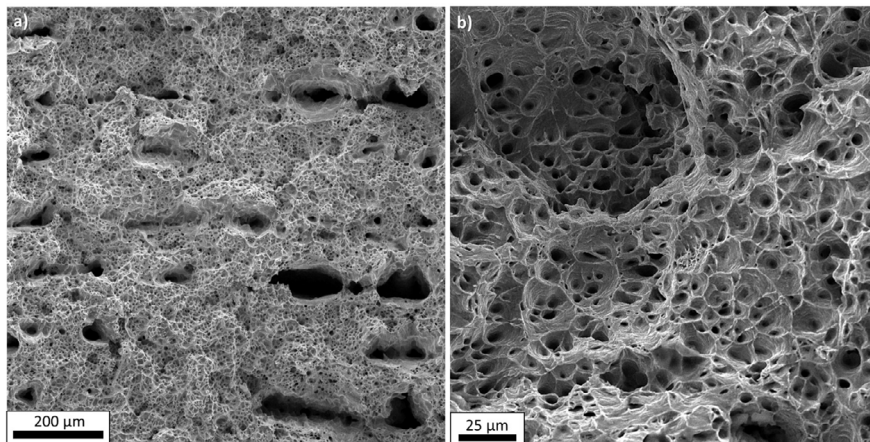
Zona di frattura duttile, a) panoramica, b) ingrandimento / Ductile fracture zone, a) overview, b) higher magnification.
